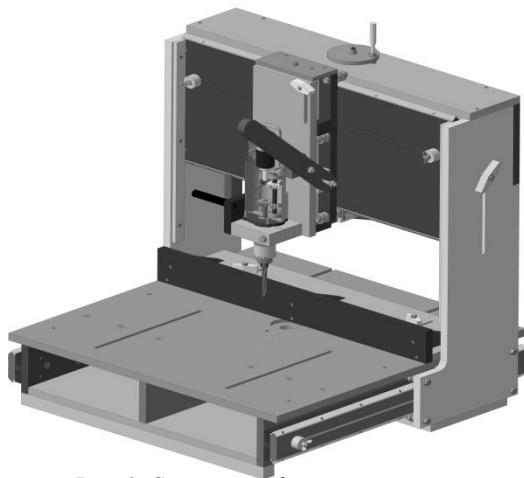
Сверлильно-фрезерный станок 3D-ROUTER
